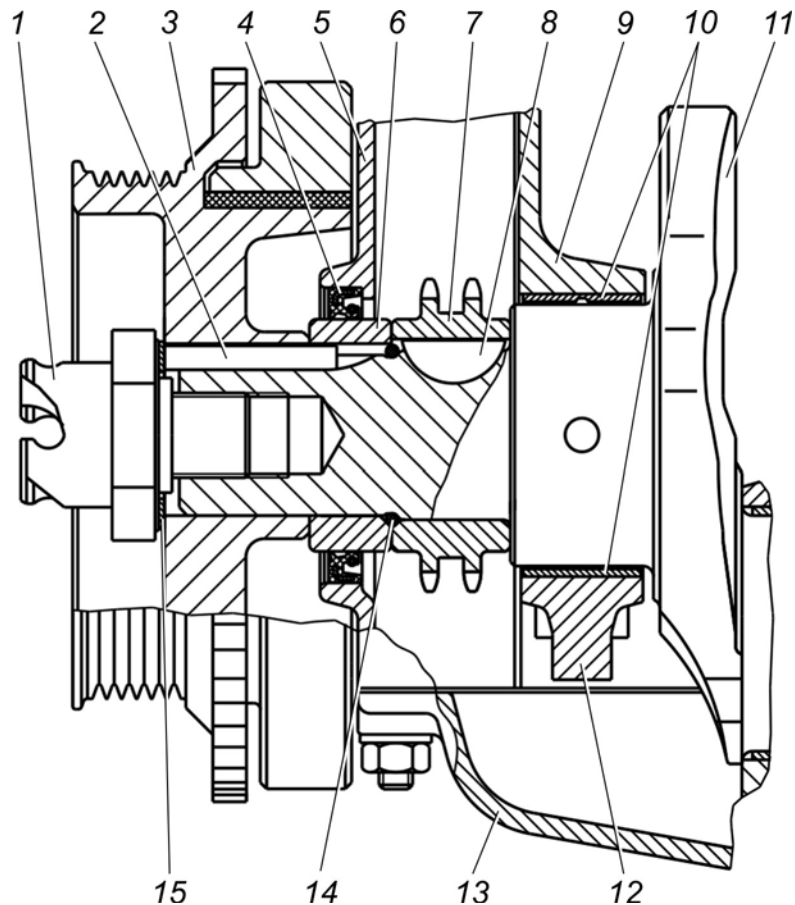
Передний конец коленчатого вала: 1 - болт (или храповик); 2 - шпонка крепления шкива-демпфера; 3 - шкив-демпфер с диском синхронизации; 4- манжета; 5 - крышка цепи; 6 - втулка; 7 - звездочка; 8 - шпонка крепления звездочки; 9 - блок цилиндров; 10 - вкладыши подшипника, 11 -коленчатый вал; 12 - крышка подшипника; 13 - масляный картер; 14 - резиновое уплотнительное кольцо; 15 -стопорная шайба храповика
